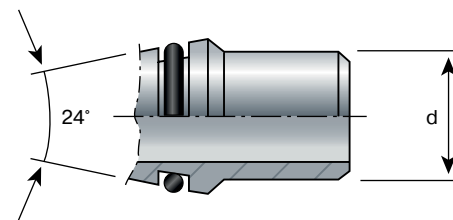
Dichtkegel 24° mit O-Ring: Form A für Schweißanschluss
